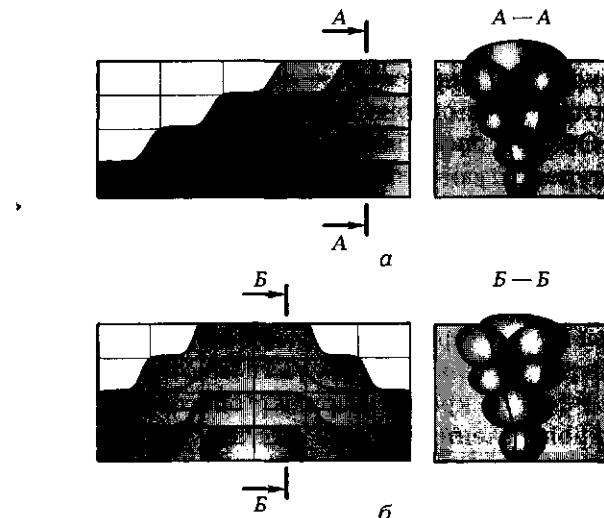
Заполнение разделки кромок при сварке деталей большой толщины каскадом (а) и горкой (б)
